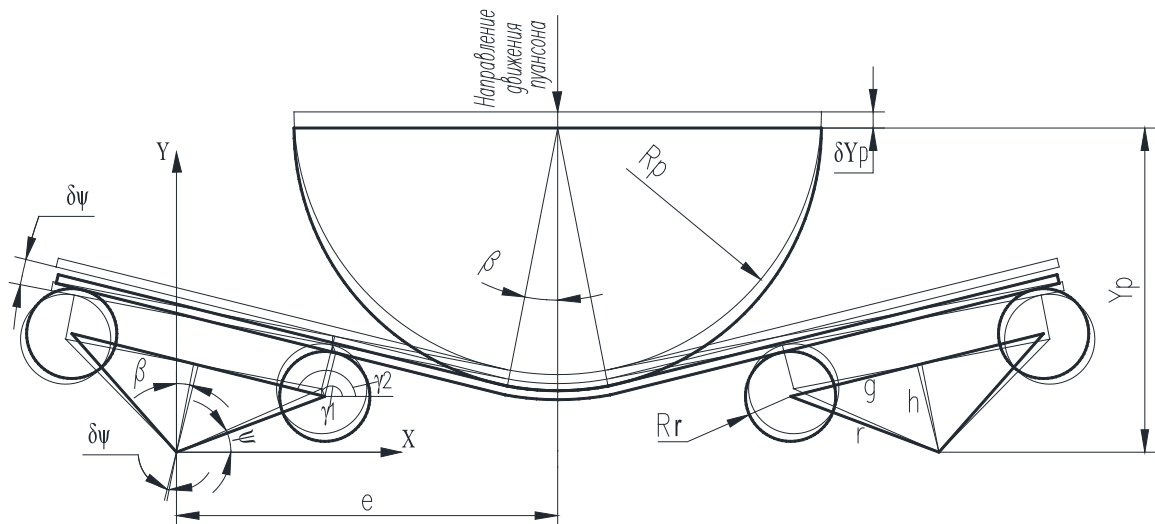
Кинематическая схема прессовой формовки с учетом упругопластического изгиба формируемой полосы
